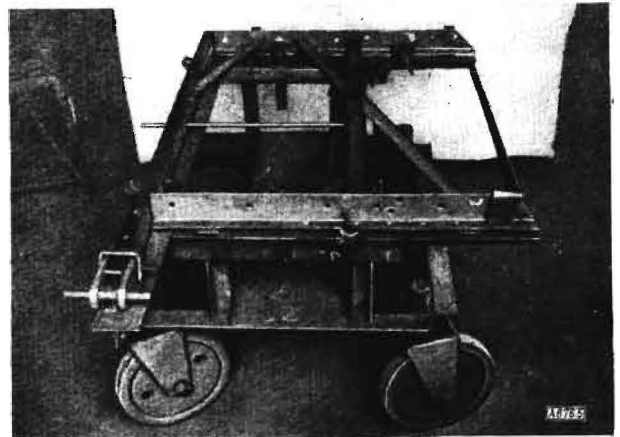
Hauptrahmen des Mähbinders in der Schweißlehre
